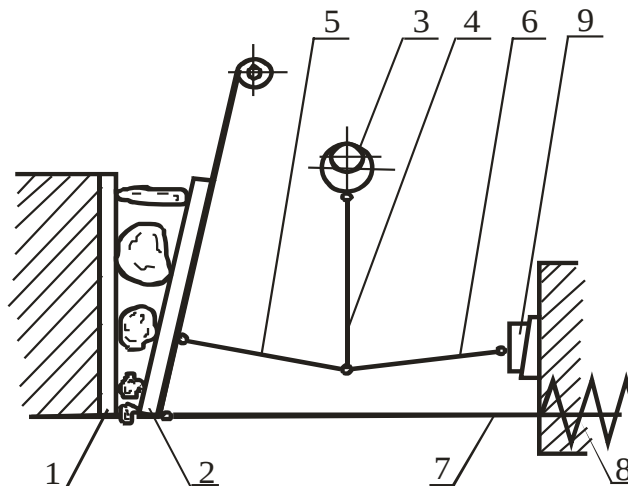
Схема щоківної дробарки з верхнім підвісом щоки.
